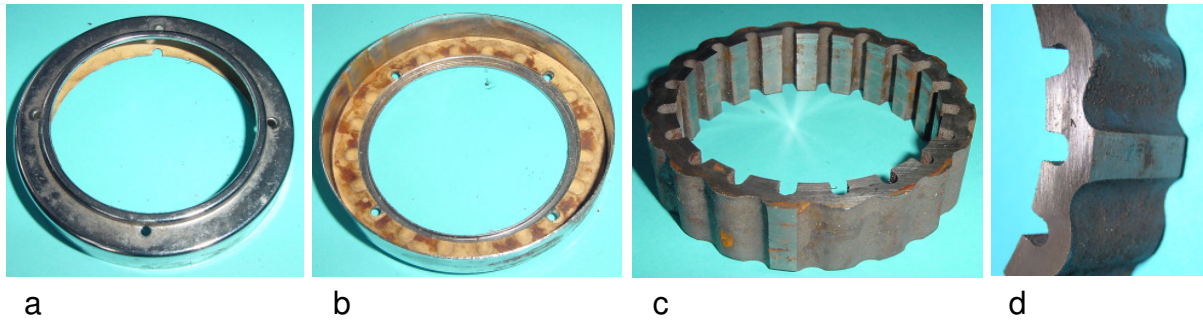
Stirnseitige Abdeckung und Halterung des Magnetrings
